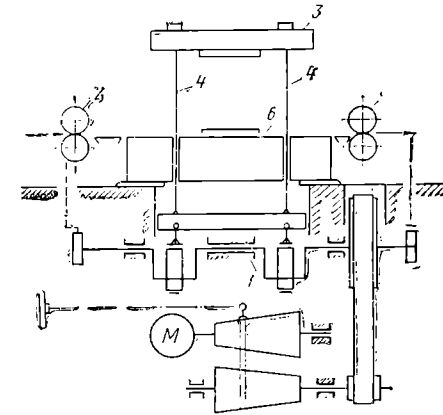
Схема многопозиционного кривошипного пресса-автомата с нижним приводом для листовой штамповки
